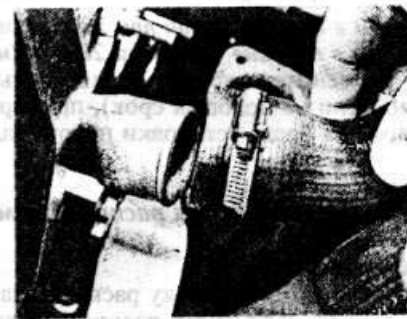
Отсоединение шланга системы охлаждения от корпуса термостата — двигатель 1,6 л
